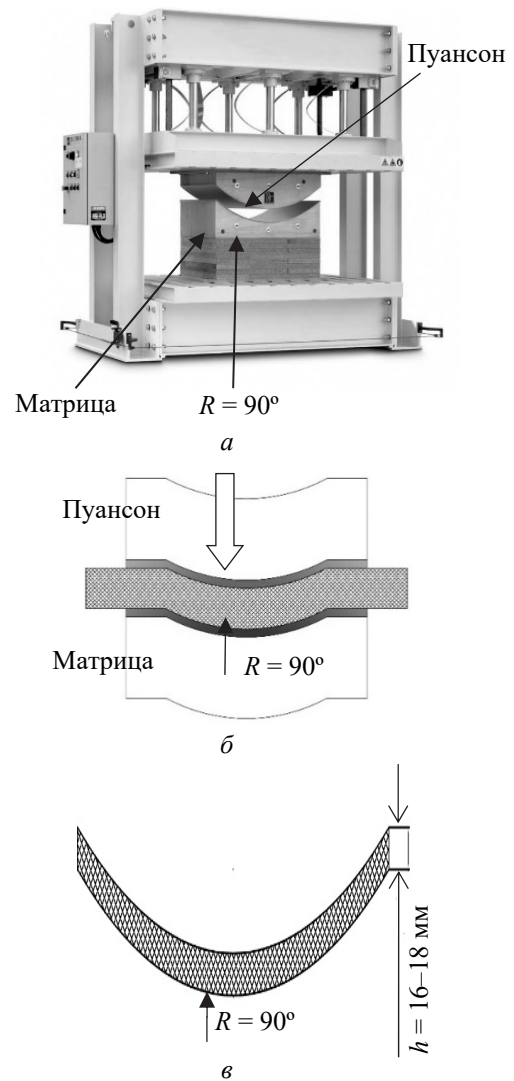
Оборудование и схема гнутья: а – пресс; б – пресс-форма; в – схема прессования
